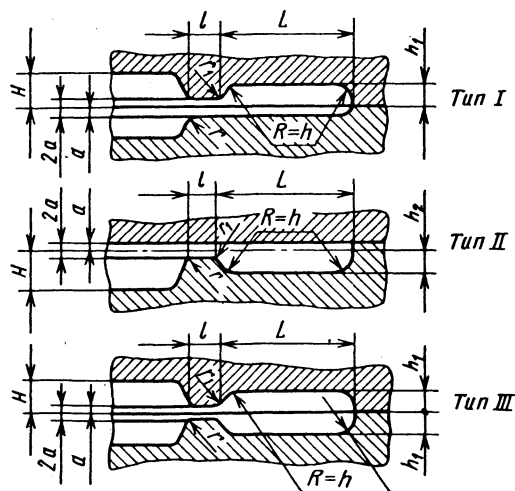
Типы и размеры облойных канавок для штампов винтовых прессов:
